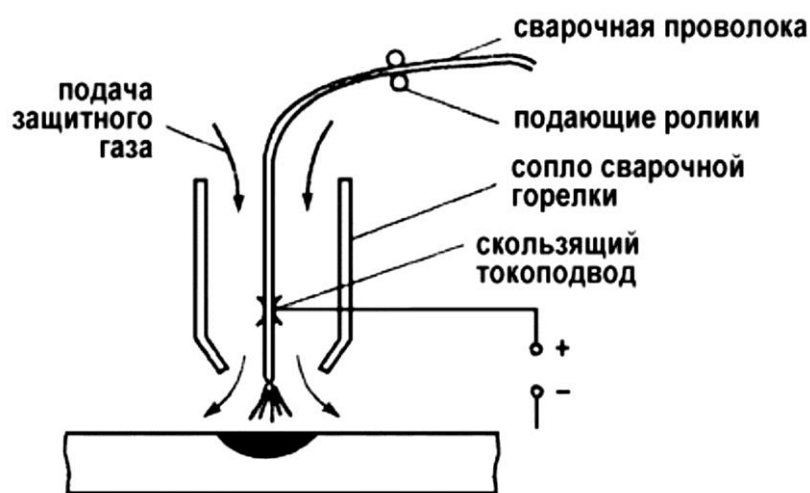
Сварка плавящимся электродом под защитой газа
